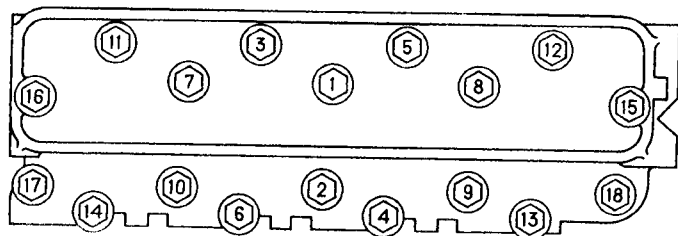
Порядок затяжки гаек головки цилиндров
